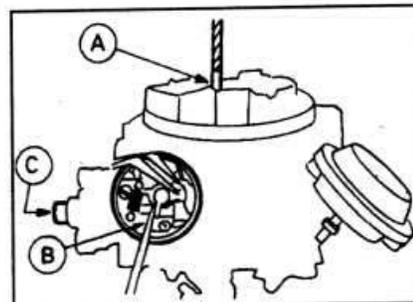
А.34. Измерение зазора воздушной заслонки. А - калиброванный стержень или хвостовик сверла, В - отвертка, С - регулировочный винт.
